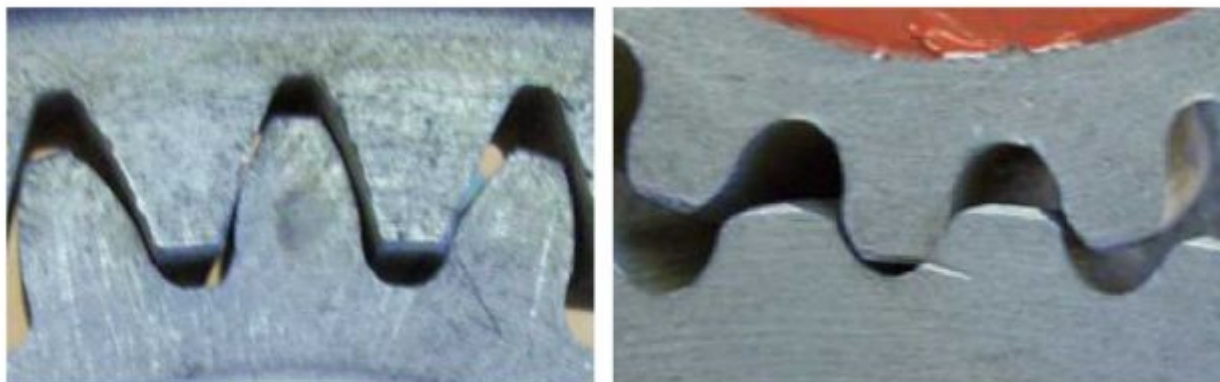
Виды зубчатых колес: с эвольвентным профилем зубьев (слева), зубчатые колеса передачи Новикова
